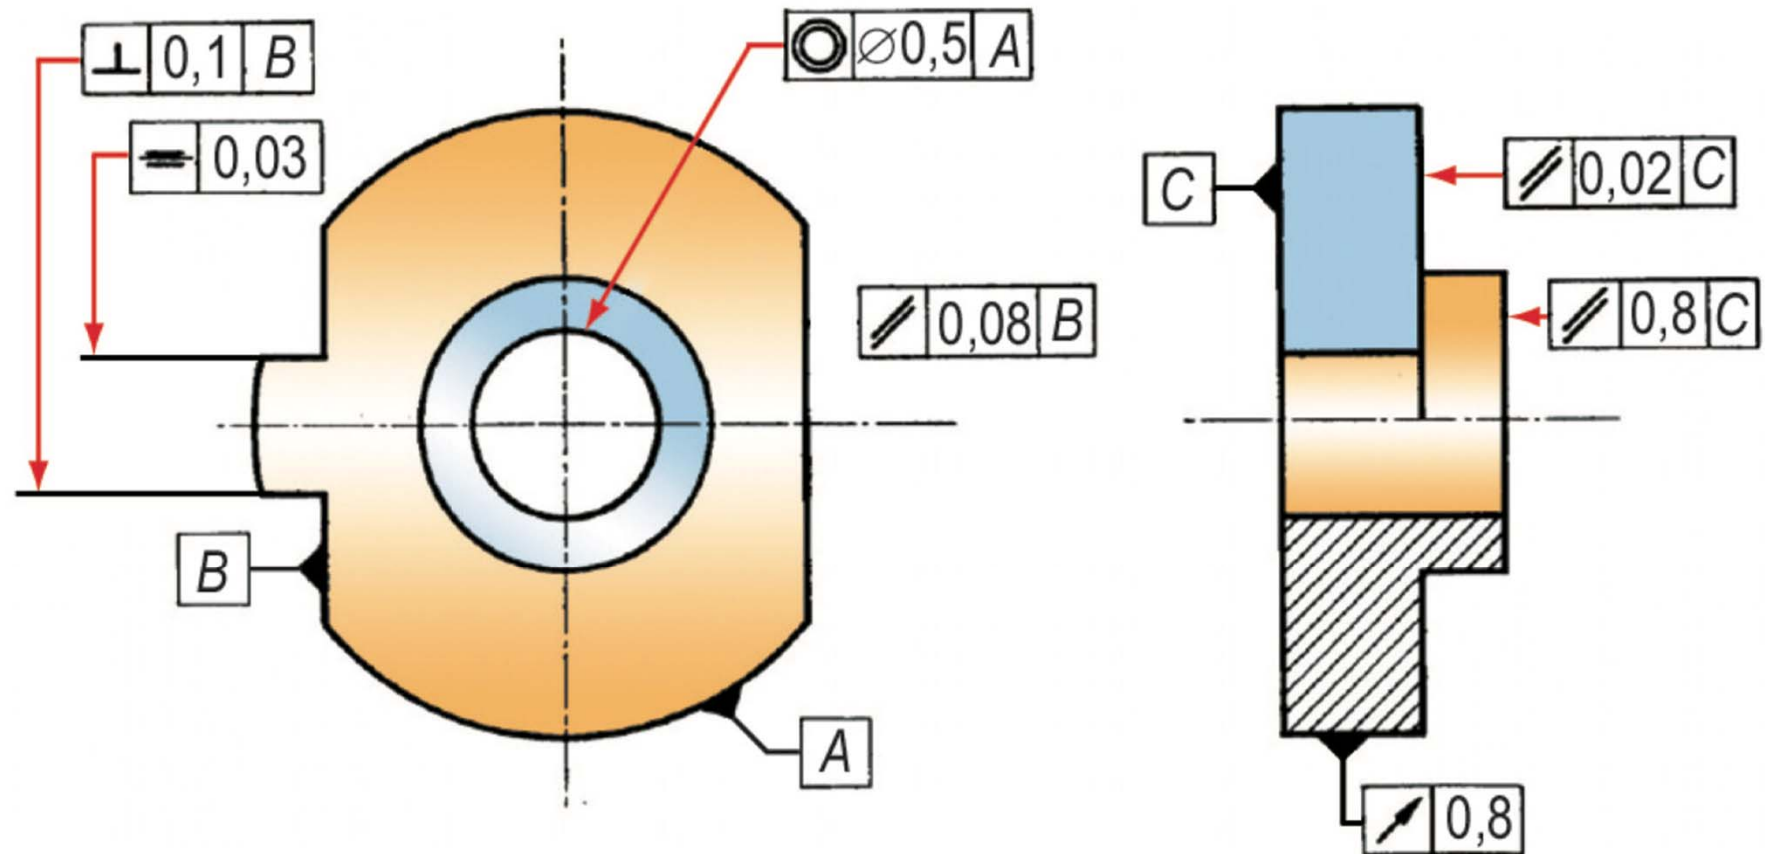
Ejemplos de especificación de tolerancias geométricas.
